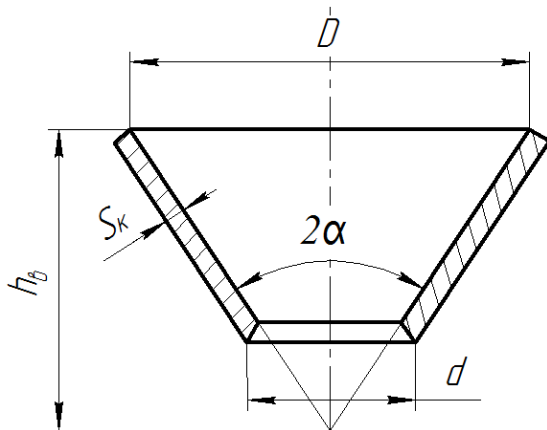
Розрахункова схема невідбортованого конічного днища
